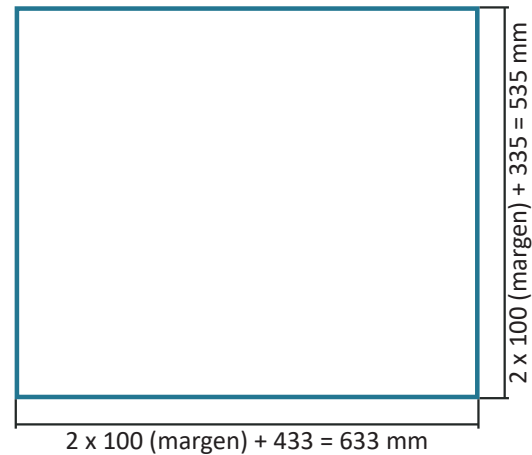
Planta de la pieza (paso entre columnas)
